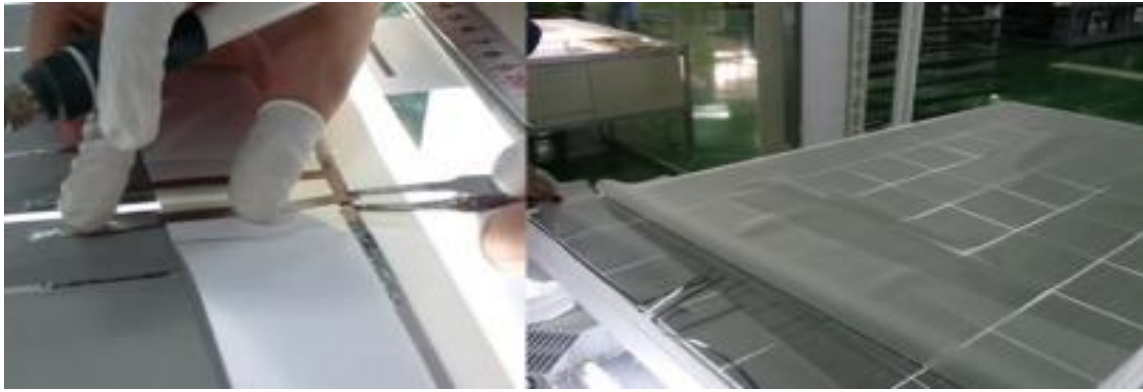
Soudage des fils sortants et couvrir EVA 2.
